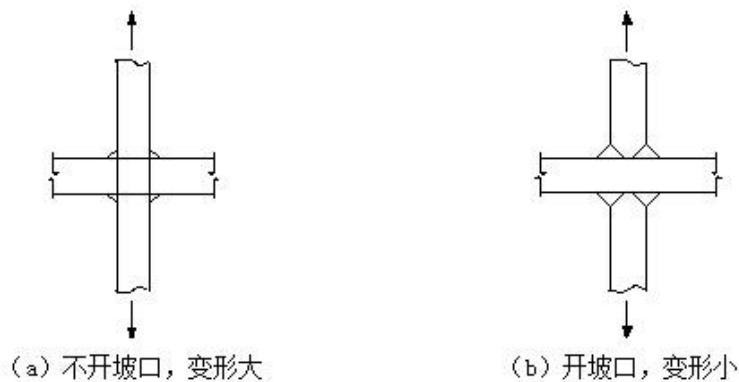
：T 形接头板厚较大时采用开坡口角对接焊缝
